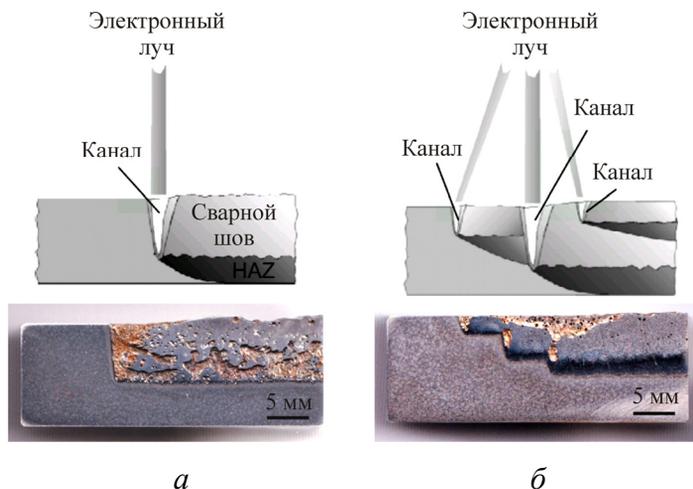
Сравнение вариантов электронно-лучевой сварки и качества сварного шва: а – одна сварочная ванна; б – три сварочных ванны [28, 29]
